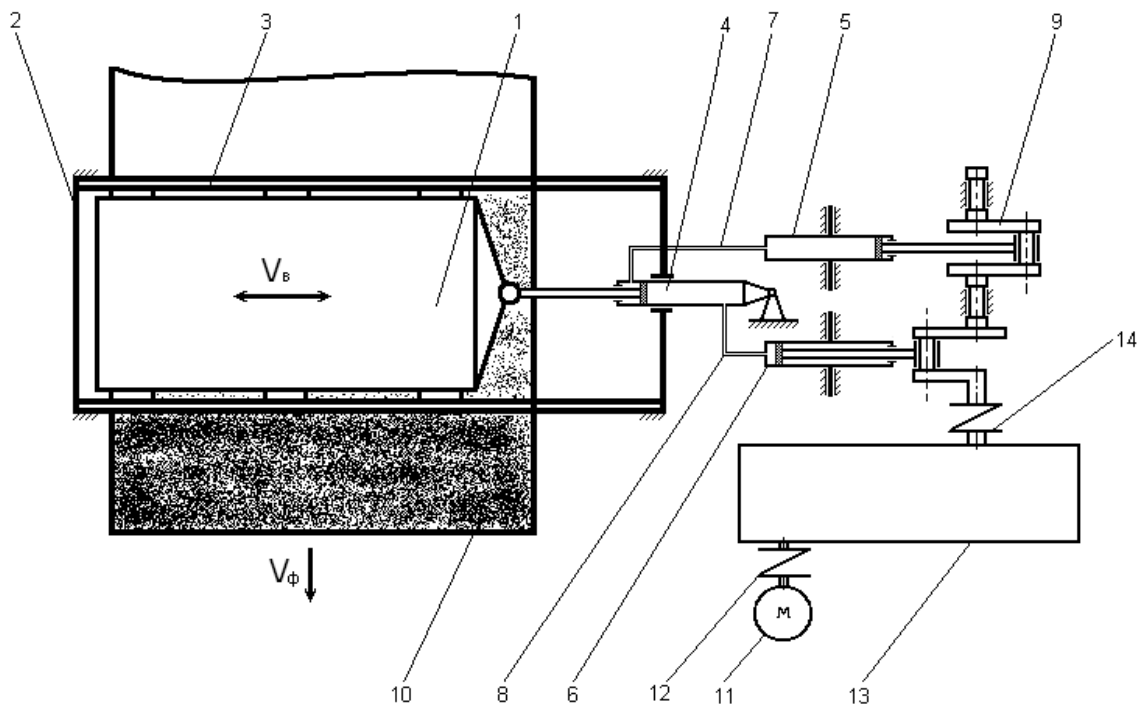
Роликова формувальна установка з гідромеханічним приводом
